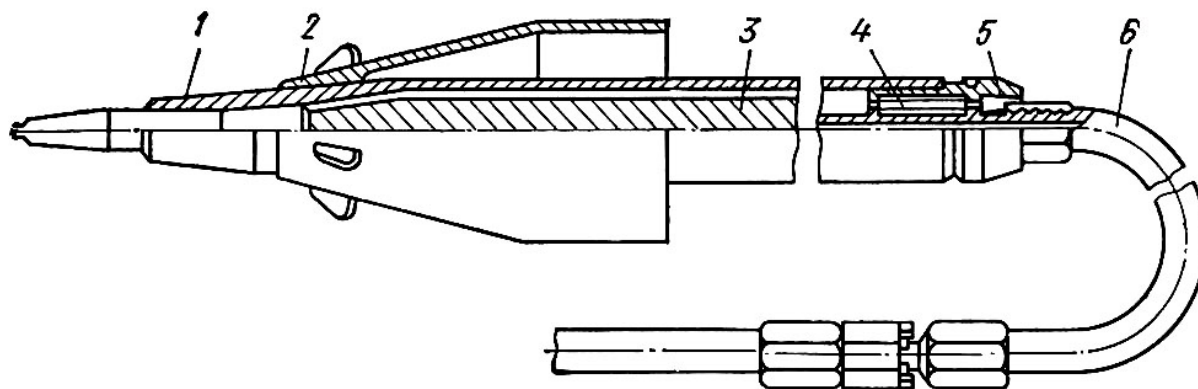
Пневмопробойник: 1 – корпус; 2 – съемный расширитель;
